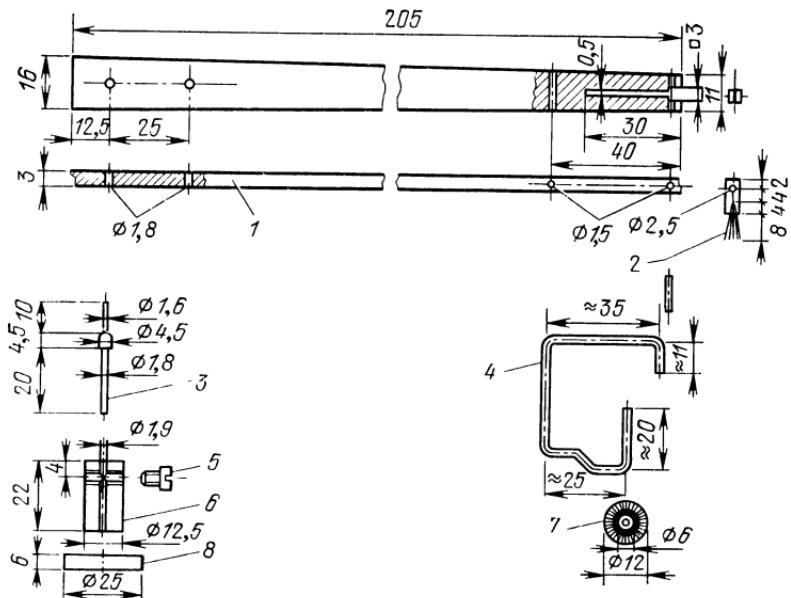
Чертежи деталей устройства для очистки пластинок:
